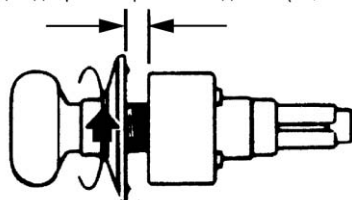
Регулировка положения розочки (С разрешения компании Schlage Lock Company)
